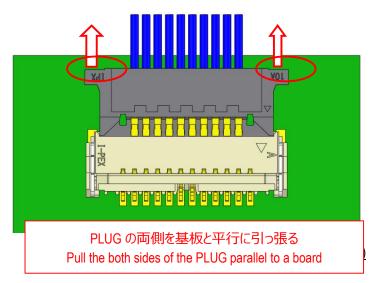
PLUG の 抜去方法 / Fig.15 To withdraw PLUG (NG)
